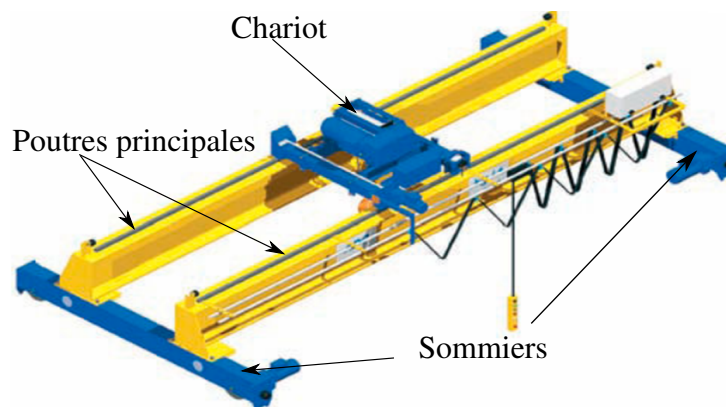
Exemple de pont roulant bi-poutre
